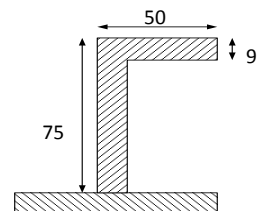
Panjang Tak ditumpu (*l*) longitudinal stiffener pada bagian Midship Kapal
